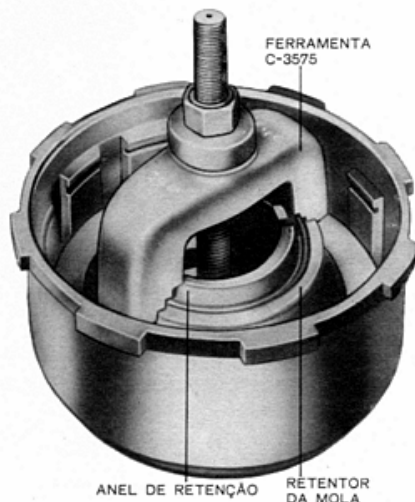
Remoção ou instalação do anel de retenção do retentor da mola da embreagem dianteira
